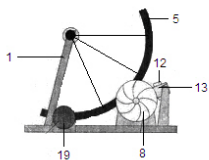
Вид регулирующего устройства со стороны крыльчатки вентилятора
